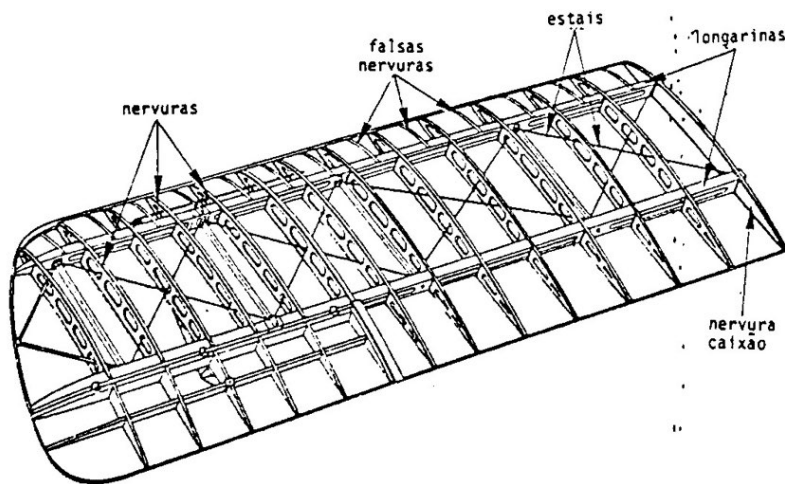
Estrutura típica das asas dos primeiros aviões (estrutura em madeira).
